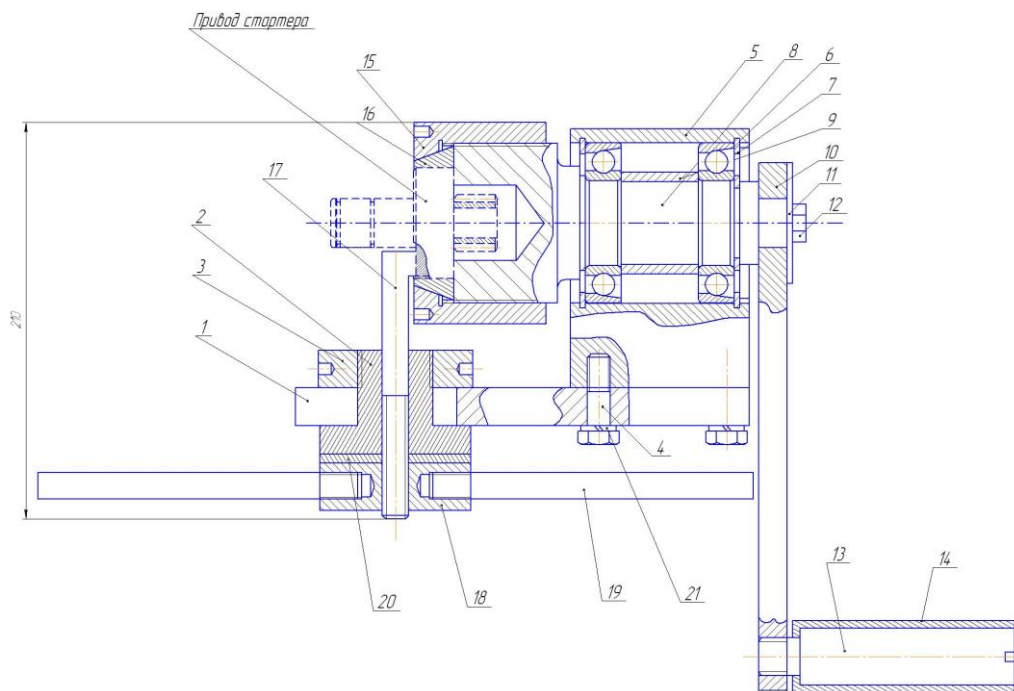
Пристрій для розбирання стартерів: 1 – плита, 2 – кондуктор, 3- циліндрична гайка, 4- болт, 5 – корпус, 6 - підшипник, 7 – стопорне кільце, 8 – вал, 9 – розпірна втулка, 10 – важіль корби, 11 – шайба утримуюча, 12 – болт, 13 – вісь, 14 – ручка, 15 – гайка, 16 – розрізна втулка, 17 – тяга, 18 – гайка, 19 – важіль, 20 – шайба, 21 – гравер.
